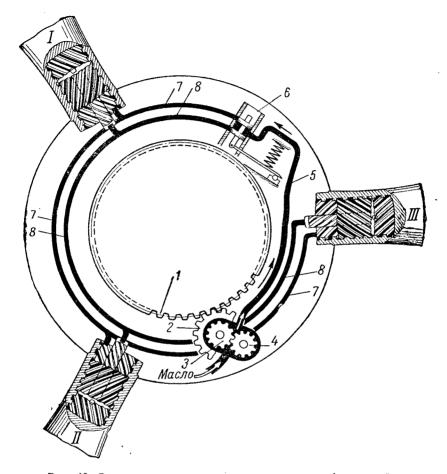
Схема расположения агрегатов втулки "Аэропроп". Шестерня 1—единственная неподвижная деталь, все остальные детали вращаются вместе со втулкой. С шестерней 1 связана приводная шестерня 2, которая сидит на одной оси с шестерней 3 маслопомпы и таким образом приводит во вращение обе шестерни и таким образом приводит во вращение обе шестерни импы 3 и 4. Масло из помпы илет под давлением по трубке 5 к регулятору 6, а отгуда по трубками 7 и 8 к обеим полостям цилиндровых групп лопастей 1, 11 и 111.
